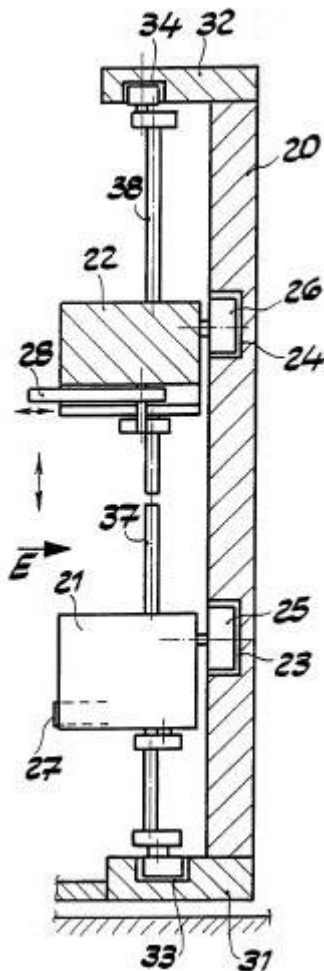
HT2, Rotorzylinder mit Steuerflächen für die Steuerstege, nach DE 19609749
